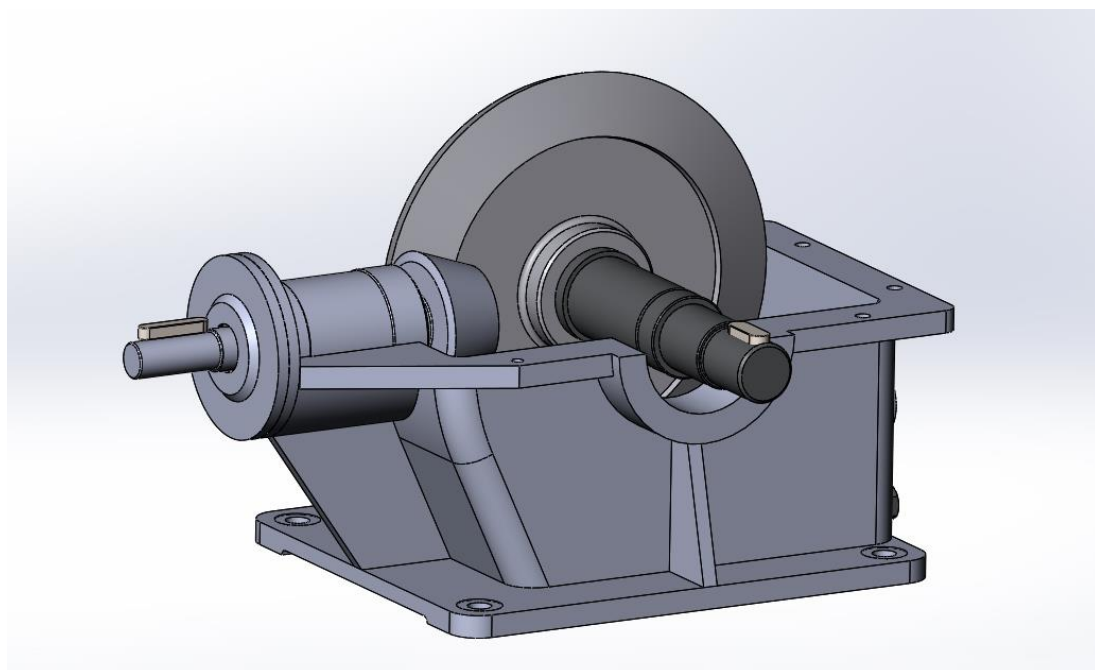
Коническая передача, воздействующая на корпус редуктора
